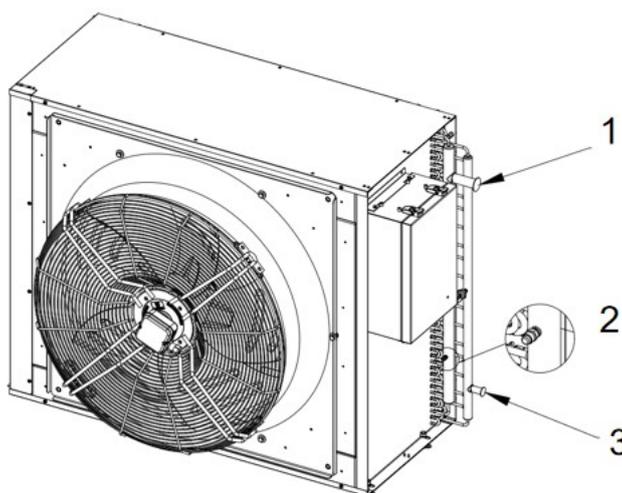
Положение клапана Шредера стандартного конденсатора
